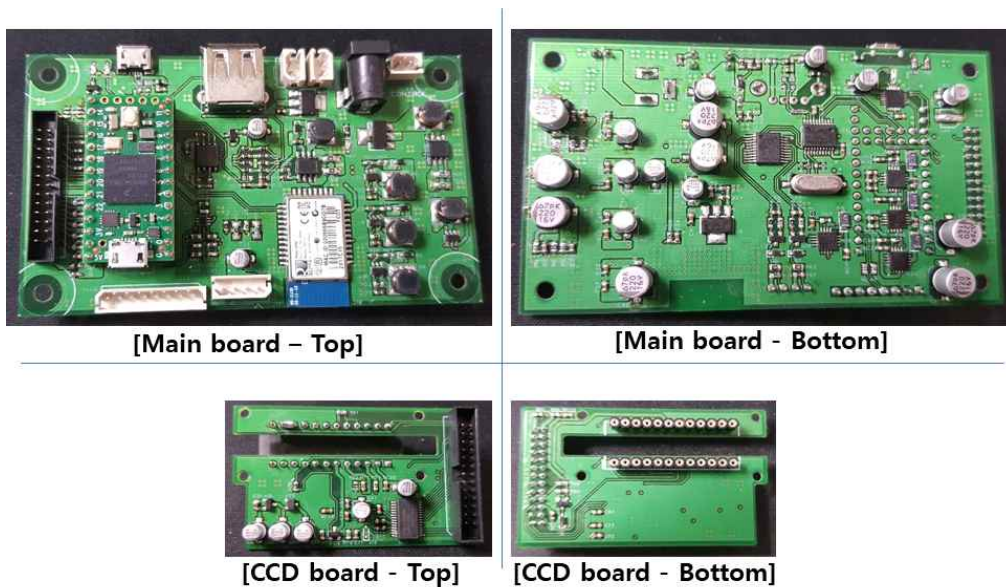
PCB Product (Top(좌) & Bottom(우)) 실물에 대한 이미지
